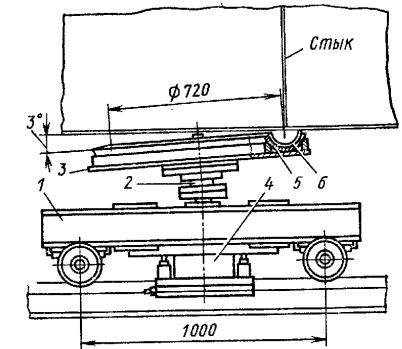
Флюсовая подушка с эластичным лотком для сварки внутренних кольцевых швов:
